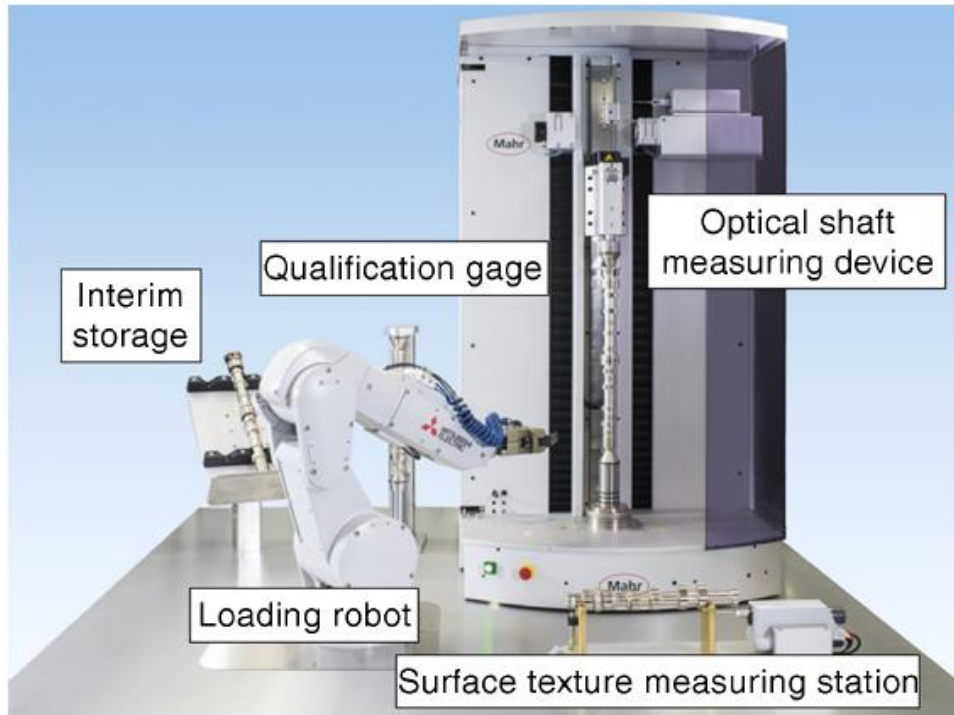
Instalación de la inspección automática completa de un árbol de levas a través de un dispositivo óptico- Fuente: "Challenges and trends in manufacturing measurement technology"-Dietrich Imkamp et al.
